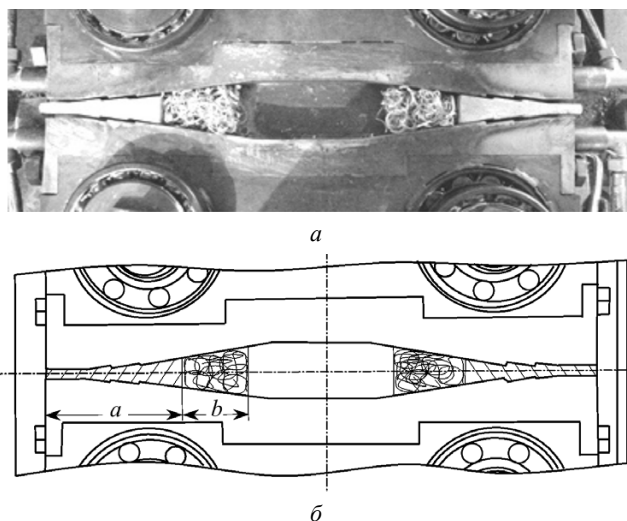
Внешний вид (а) и схема (б) кристаллизатора УГЛДМ с образцами для исследований
